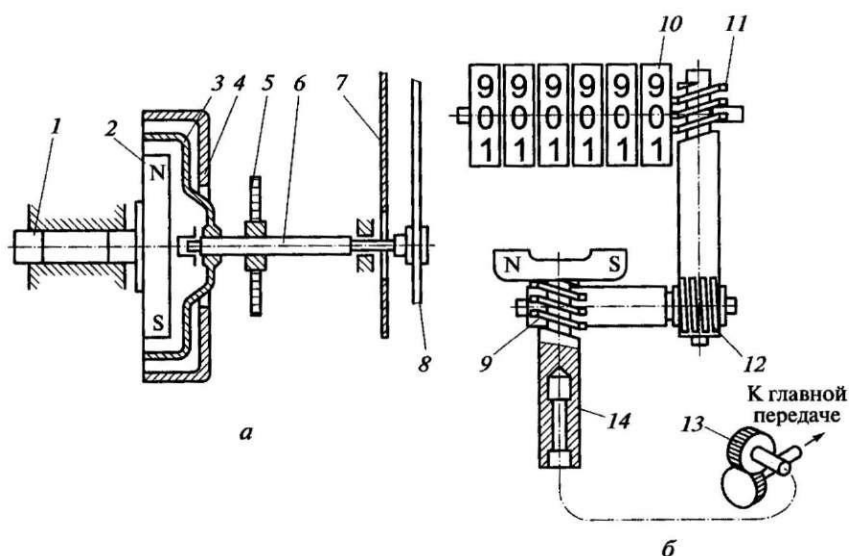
Схема действия спидометра с приводом от гибкого вала: а — магнитоиндукционный скоростной узел; б — привод счетного узла; 1 — приводной валик; 2 — постоянный магнит; 3 — алюминиевая катушка; 4 — магнитный экран; 5 — возвратная пружина; 6 — ось стрелки; 7 — шкала; 8 — стрелка; 9 — ведущий червяк; 10 — начальный барабанчик счетного узла; 11 — ведомый червяк; 12 — промежуточный червяк; 13 — винтовой редуктор; 14 — входной валик
